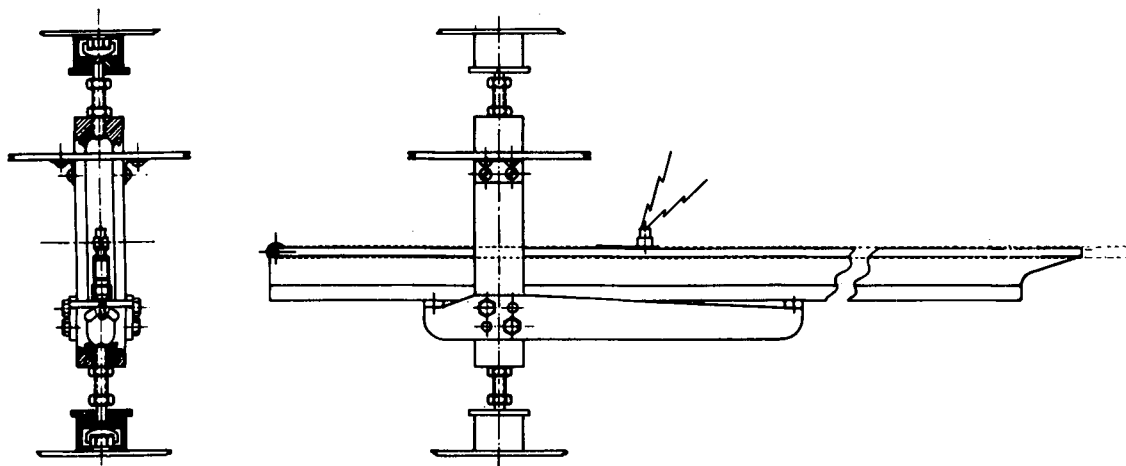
Soporte de la bobina del fluxímetro electrónico
